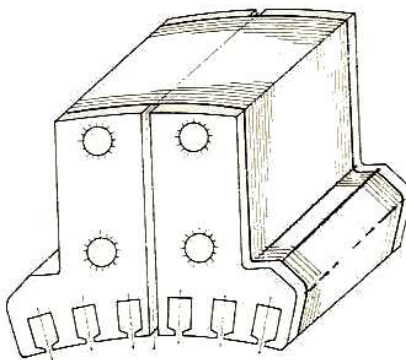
Zapojení hlavních budících pólů trakčního motoru TE 005, převzato z [6]
